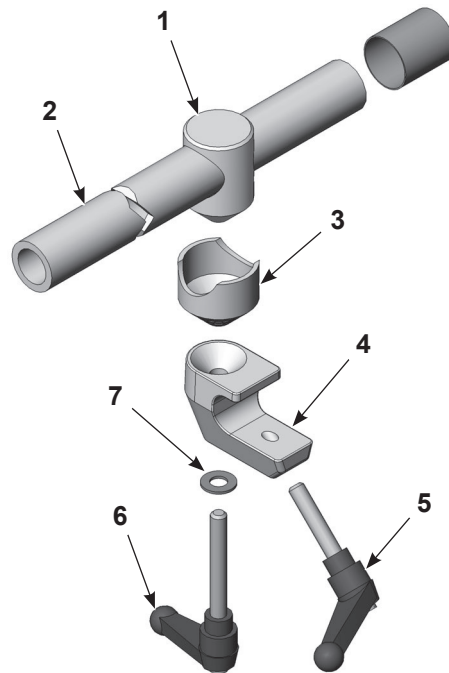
Uchwyt do pistoletów mocowanych na rurze w rowku T
